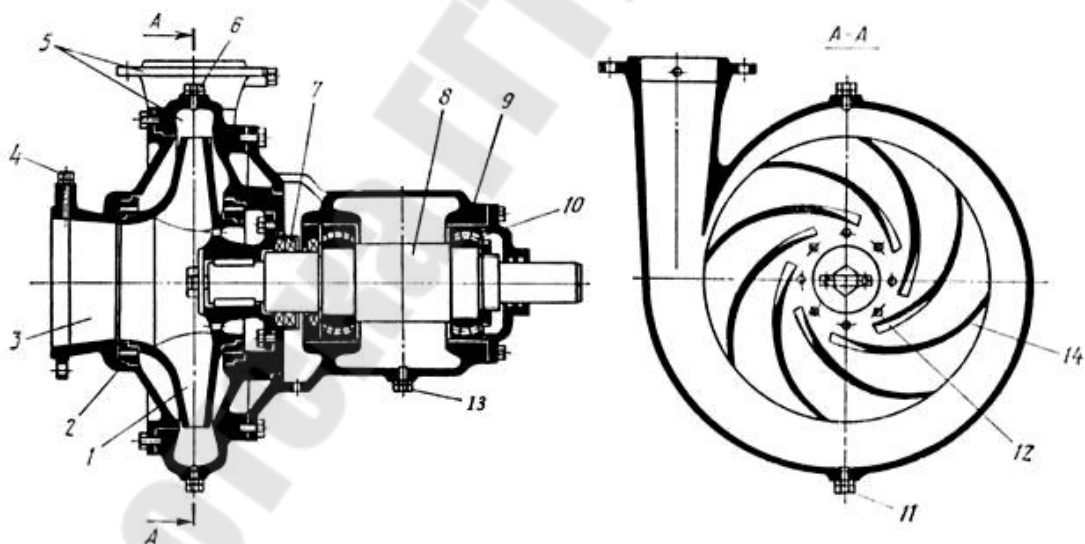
Центробежный одноступенчатый горизонтальный насос типа *К
